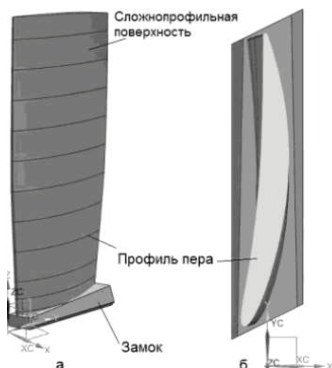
Лопатка компрессора и измеряемые сечения пера
